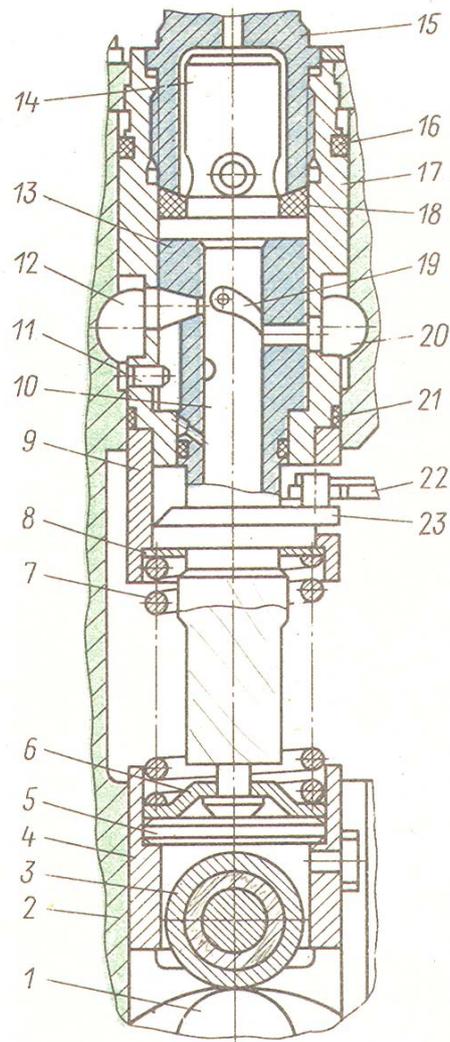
Схема подачи топлива в цилиндр дизеля ТНВД с плунжером золотником: 1 – кулачок распределительного вала; 2 – корпус насоса; 3 – ролик толкателя; 4 – толкатель; 5 – пята толкателя; 6 – тарелка пружины; 7 – пружина; 8 – опорная шайба; 9 – опорная втулка; 10 – плунжер; 11 – штифт; 12 – впускное отверстие; 13 – втулка плунжера; 14 – нагнетательный клапан; 15 – штуцер; 16 и 21 – уплотнительные кольца секций; 17 – корпус секций насоса; 18 – шайба; 19 – спиральная канава плунжера; 20 – перепускное отверстие; 22 – рейка; 23 – поворотная втулка плунжера;
